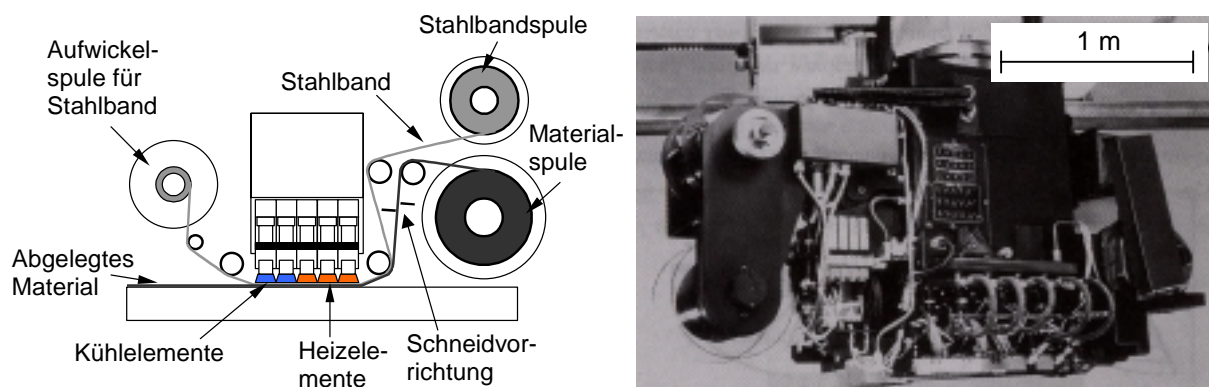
Prinzip a) und Bild b) des Thermoplast-Tapelegekopfes von Cincinnati Machine [63]
